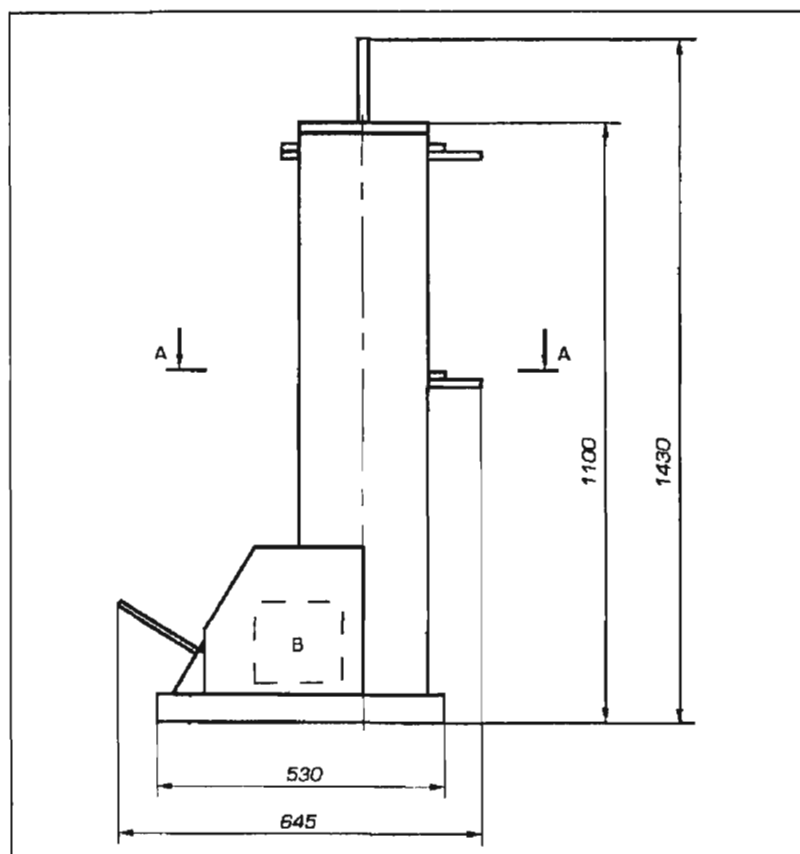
Габаритные размеры выключателя ВВСВ-27,5-25/630-1600
